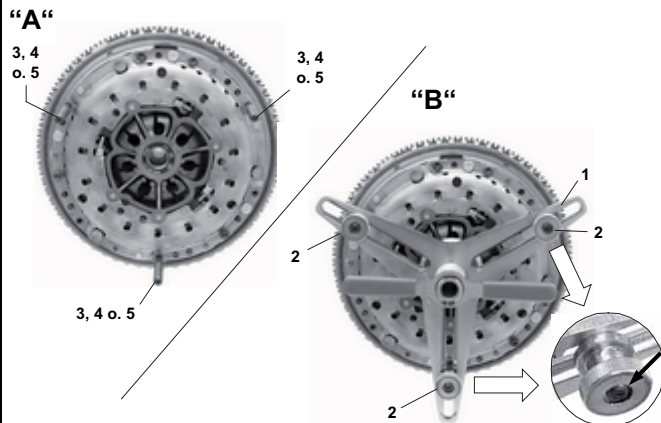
Druckspindel eindrehen, Befestigungsschrauben herausdrehen.
